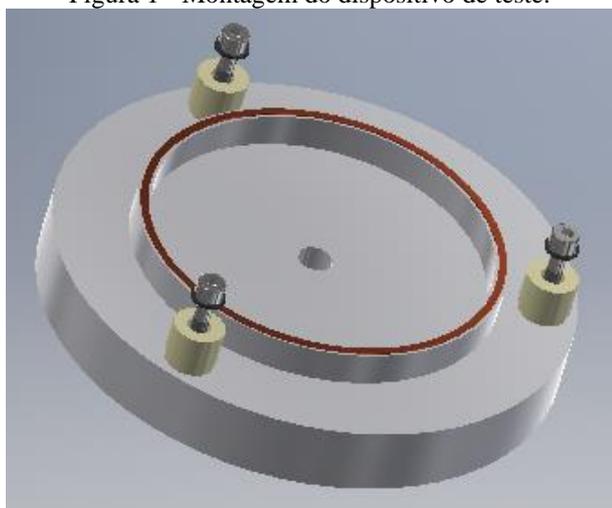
Montagem do dispositivo de testes sem tampa superior.
